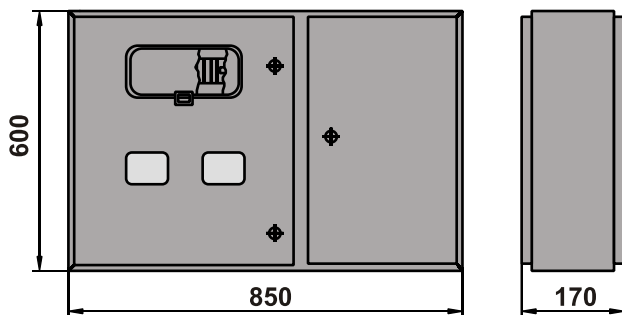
Внешний вид и габаритные размеры ЩЭЗО-2200Н
